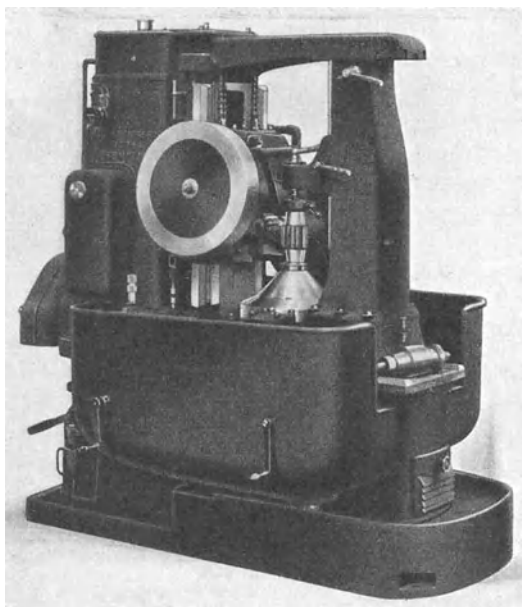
Abwälzfräsmaschine in starrer Sonderausführung für Automobilgetrieberäder. (Pfauter, Chemnitz.)
